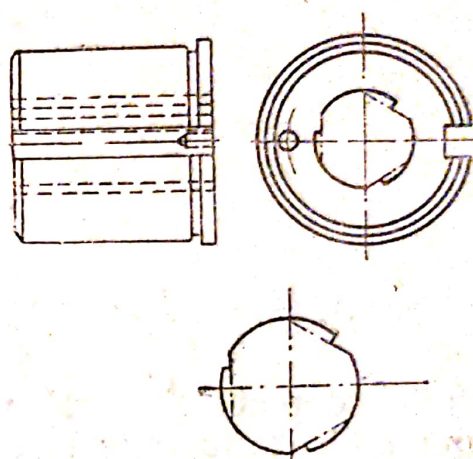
Construcția bușcilor rotative la automate cu tarod fix
